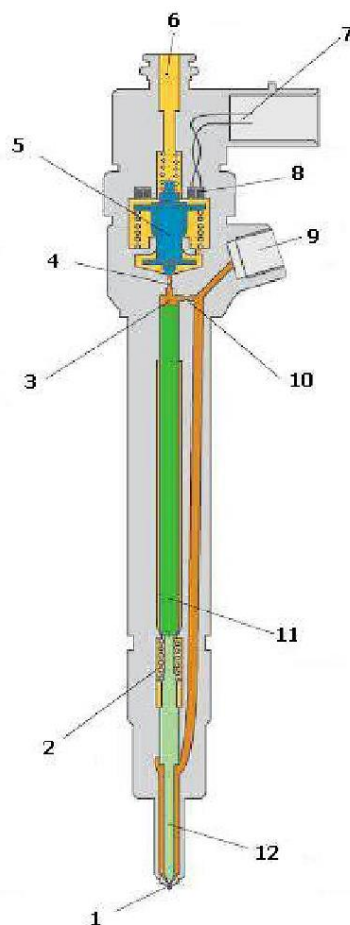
Пристрій електрогідравлічної форсунки: 1 – сопло форсунки; 2 – пружина; 3 – камера керування; 4 – зливний дросель; 5 – явір електромагніту; 6 – зливний канал; 7 – електричний роз'єм; 8 – обмотка збудження; 9 – штуцер підведення палива; 10 – впускний дросель; 11 – поршень; 12 – голка форсунки.
